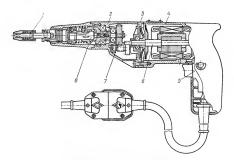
Электрошуруповерт ИЭ-3601Б: — отвертка: 2— корпус редуктора: 3— промежуточный цит; 4— корпус электродвигатель; 5— выключатель; 6— электродвигатель; 7— редуктор; 3— удариый механизм
